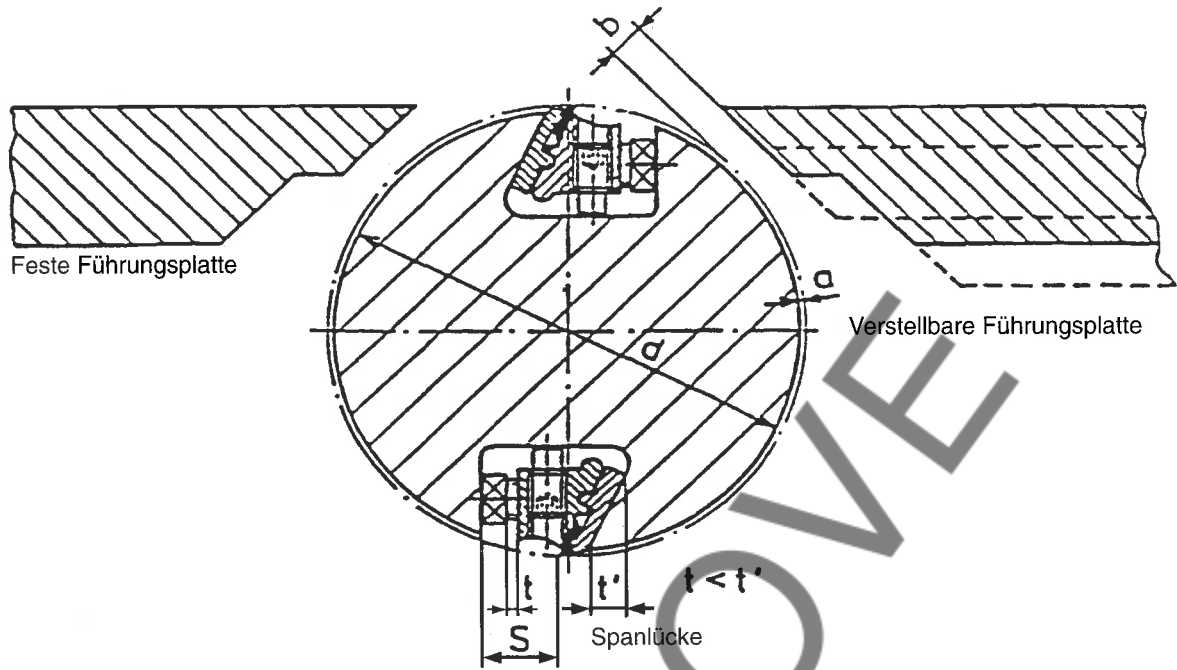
Messerwelle mit Abmessungen und Luftstrecken
